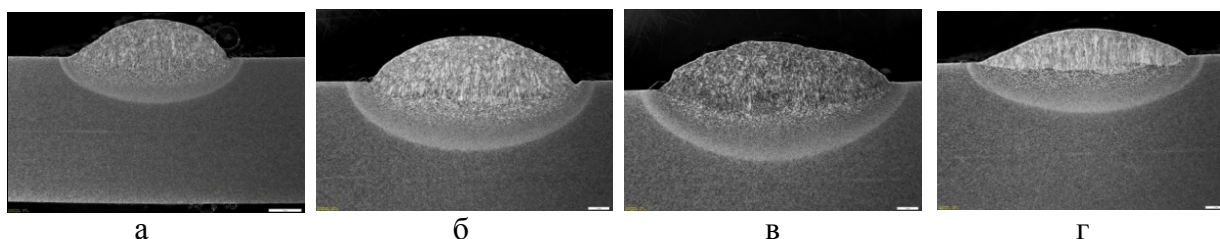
Макрошлифы сварных швов и неметаллические включения в наплавленном металле по ГОСТ 1778-70: а - наплавка электродами №1 (P1), балл НВ V; б - наплавка электродами №7 (P7), балл НВ III; в - наплавка электродами №8 (P8), балл НВ IV; г - наплавка электродами №9 (Phoenix), балл НВ III
